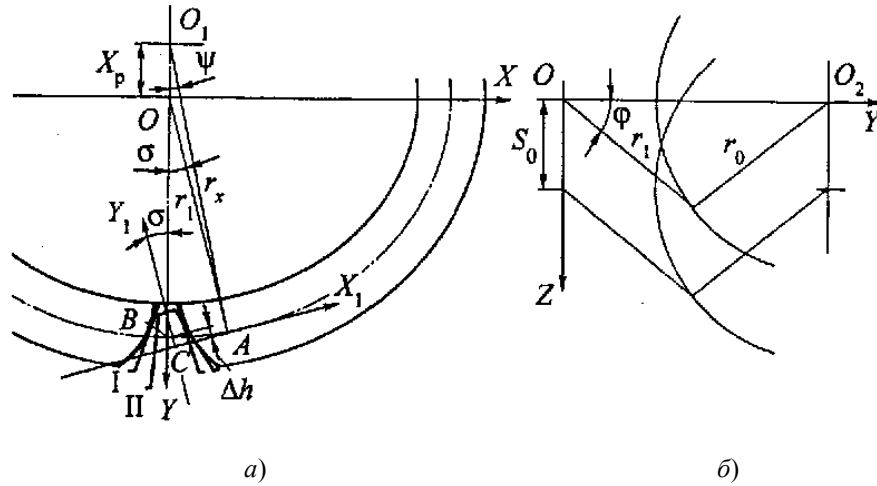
Схема к расчету процесса формообразования инструментами реечного типа
